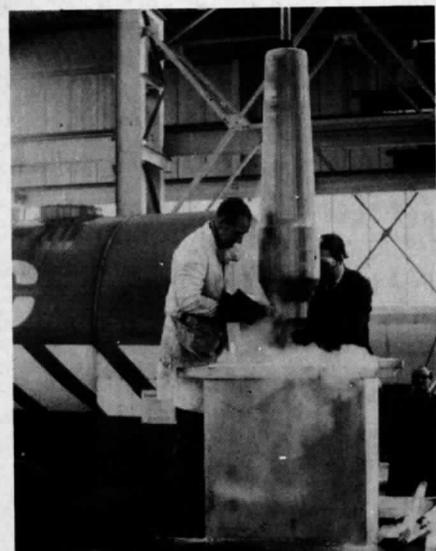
Arbre pour machine à concasser les minerais prêt pour l'assemblage.
